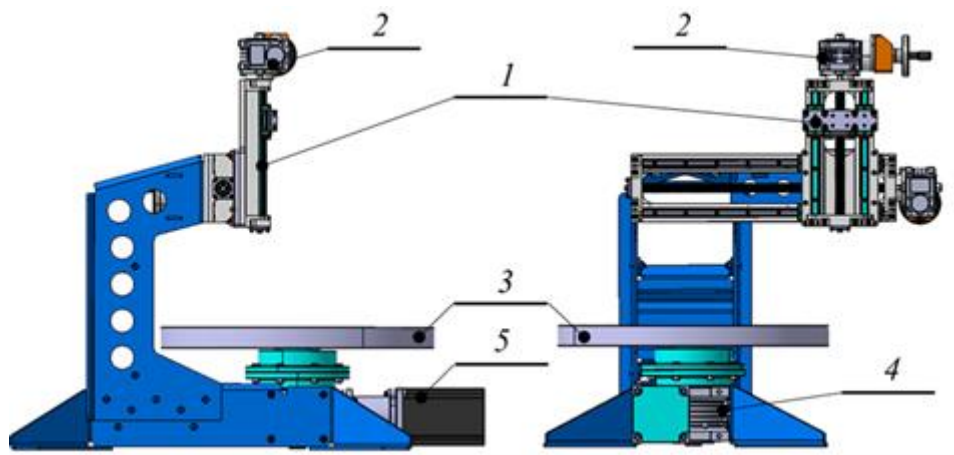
Установка для об'ємного деформування заготовок конічних секцій КПО.
